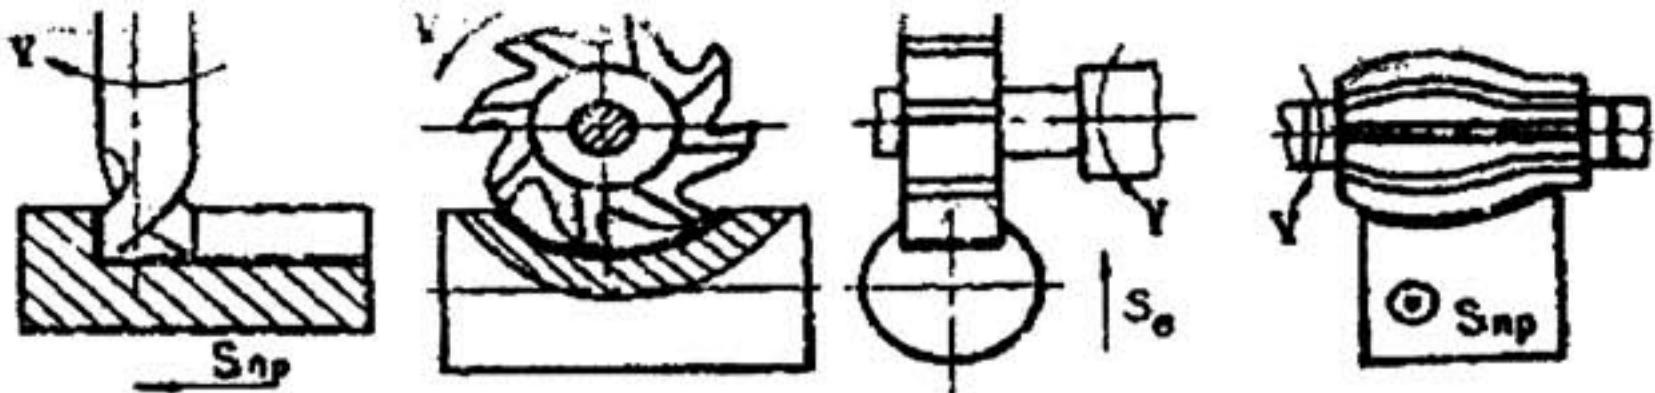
Схемы обработки поверхностей заготовок на универсально-фрезерных станках
